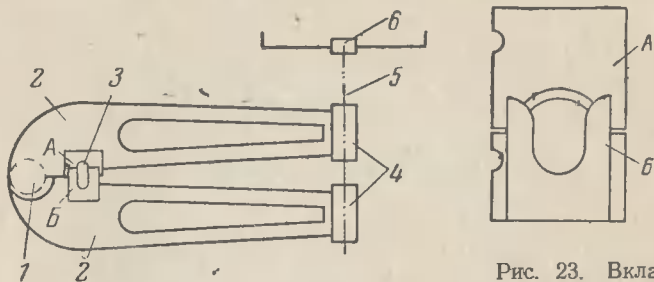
Схематический чертеж клещей типа МИ-19А.
